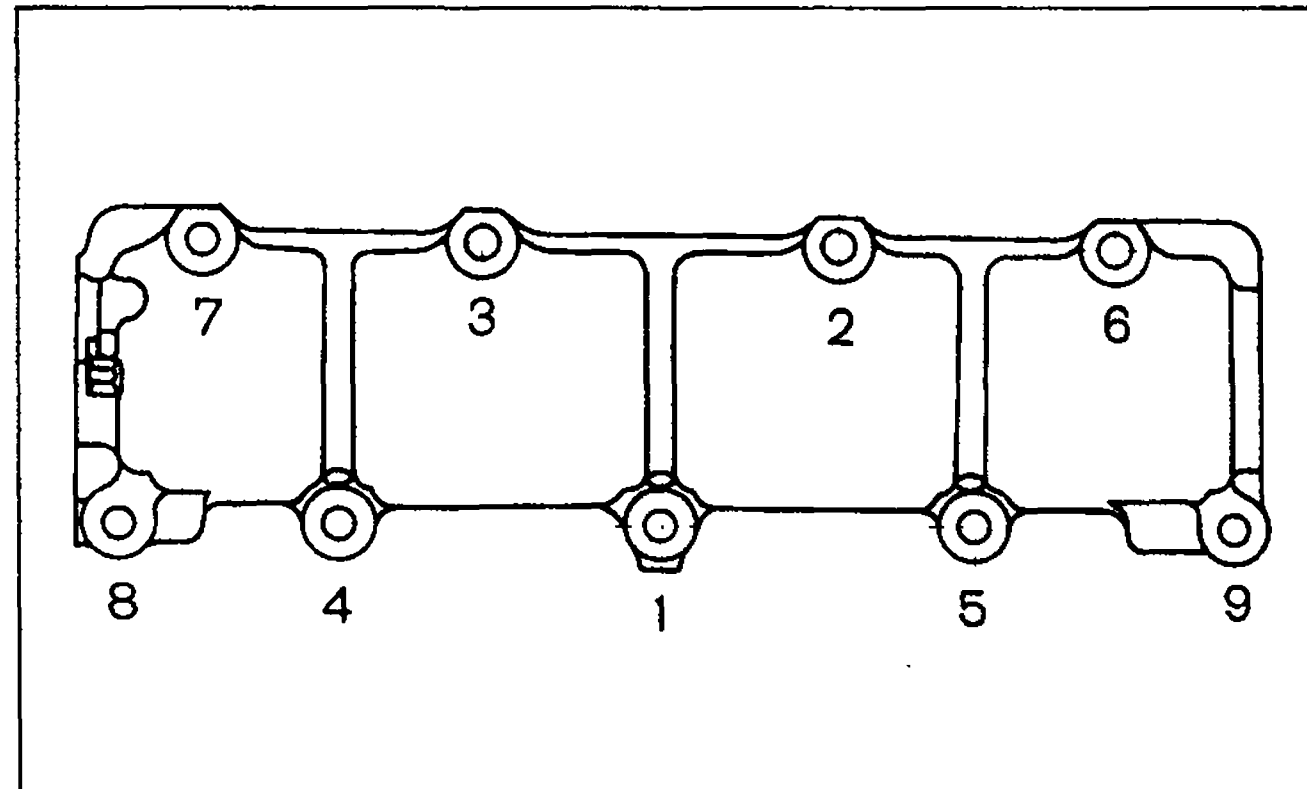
Порядок затягивания гаек корпуса подшипников распределительного вала
